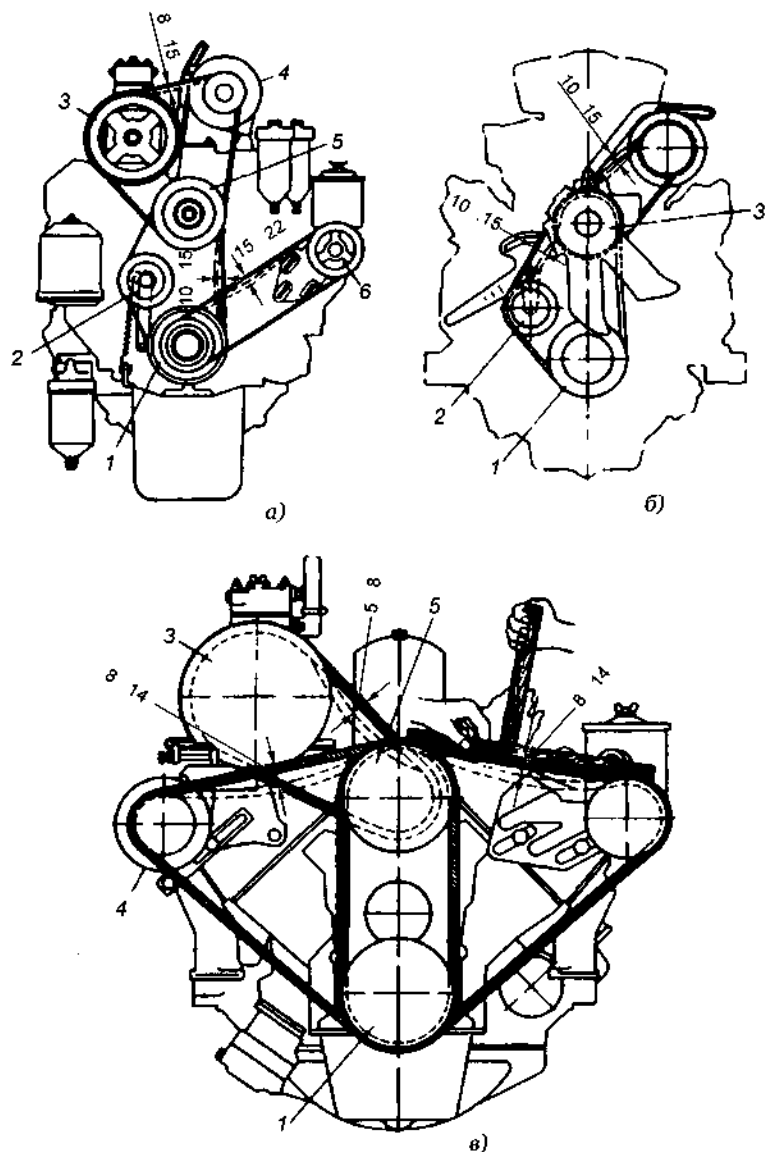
Проверка натяжения приводных ремней двигателя (расположение агрегатов): 1 — шкив коленчатого вала; 2 — натяжной шкив (ролик); 3 — шкив компрессора; 4 — шкив генератора; 5 — шкив жидкостного насоса и вентилятора; 6 — шкив насоса гидроусилителя рулевого управления
